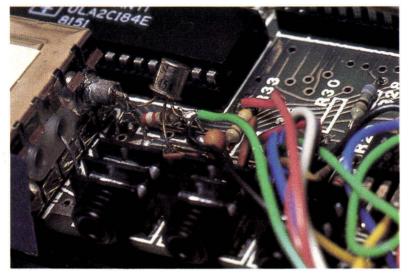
Le transistor, monté en «émetteur suiveur», est soudé à proximité de modulateur
